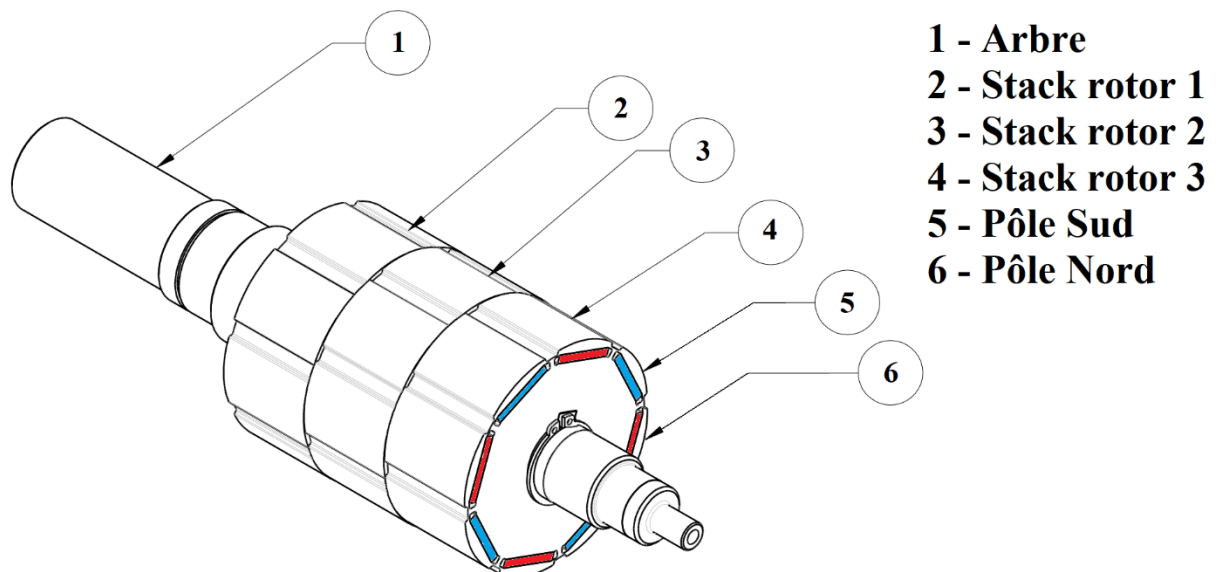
Plan du rotor de la machine triphasée à douze enroulements.
